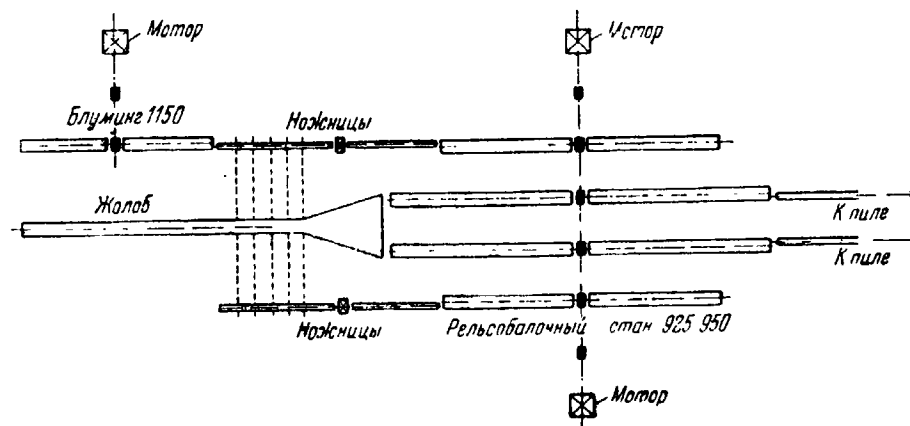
Реверсивный рельсобалочный стан 925—950 с двумя двигателями
